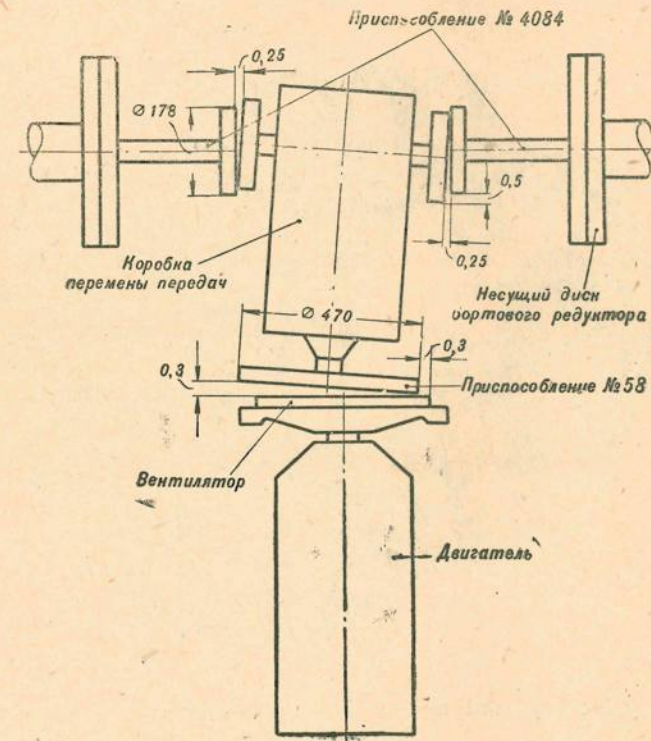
Схема установки коробки перемены передач по двигателю и бортовым передачам
